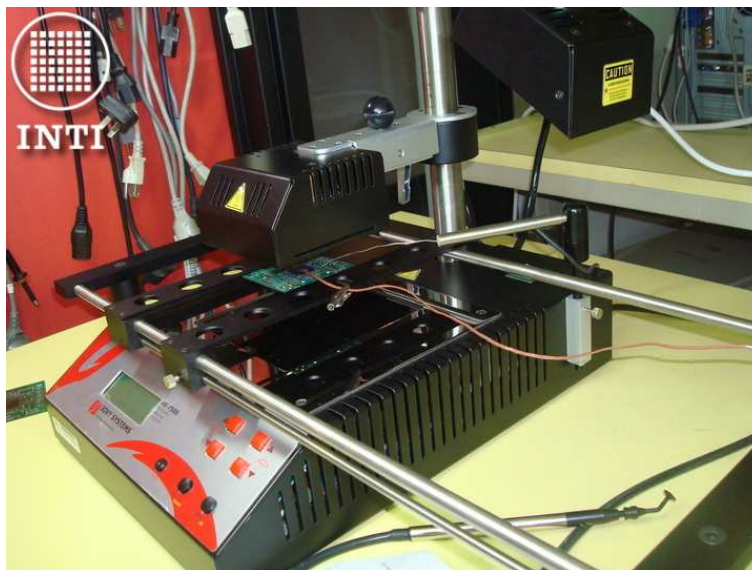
Proceso de soldadura, con ambos calefactores (superior e inferior) aplicados.
